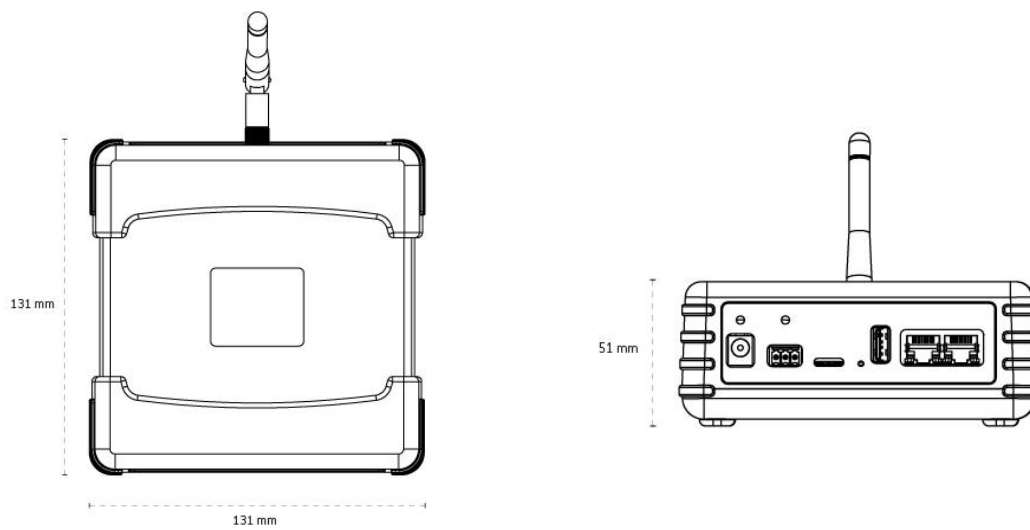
Dimensões do Universal IoT Gateway com caixa de ABS.
